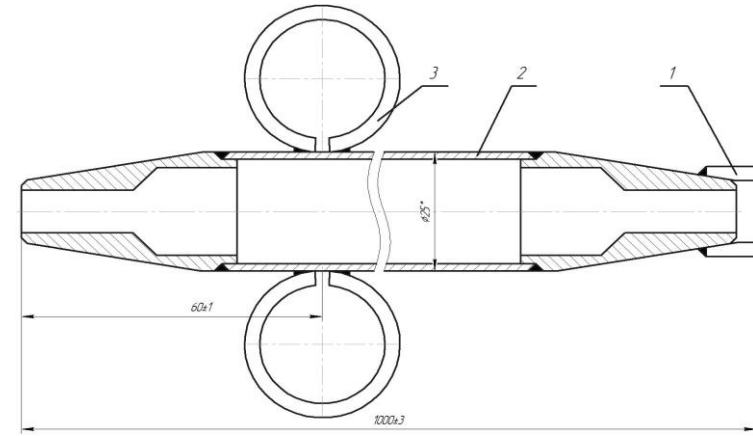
Пробоотборник ПН-6. 1 – ножка; 2 – трубка с конусами; 3 – ушко.
